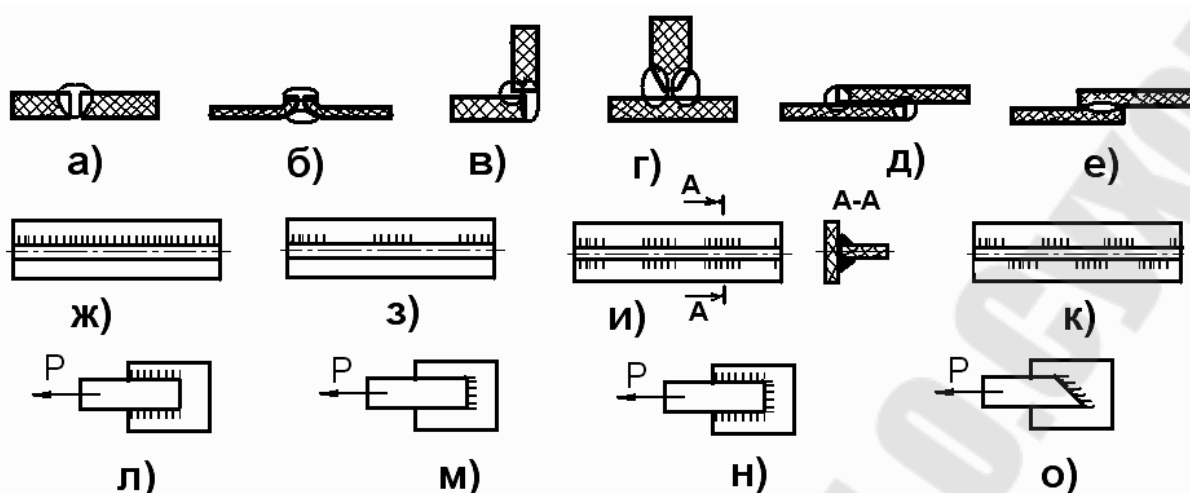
Конструктивные исполнения сварных соединений
